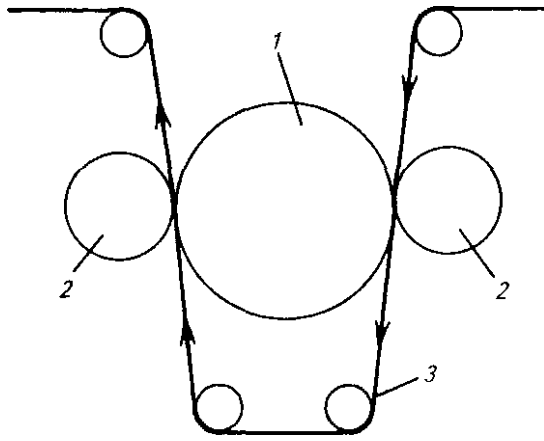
Схема лощільного каландра: 1 — хромований циліндр; 2 — притискні вали; 3 — папероведучий валик
